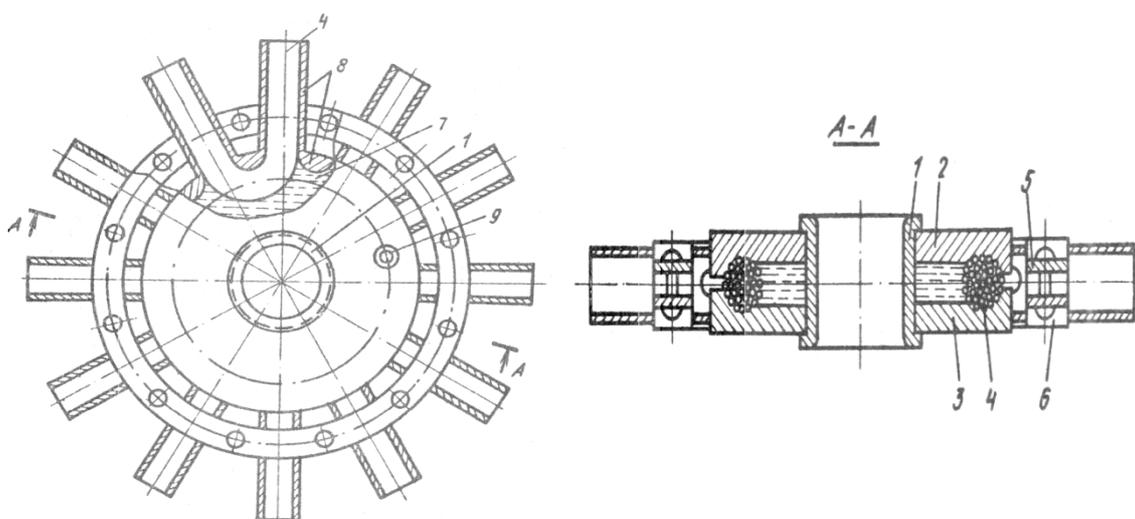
Схема радиальной щётки цилиндрической формы с U-образными пучками ворсовых элементов и кольцевой камерой для пластичного смазочного материала
